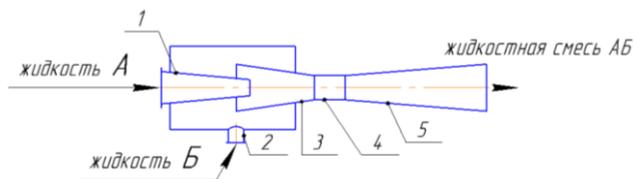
Конструкция эжектора: 1 — сопло; 2 — всасывающий патрубок; 3 — камера смешивания; 4 — горловина; 5 — диффузор
